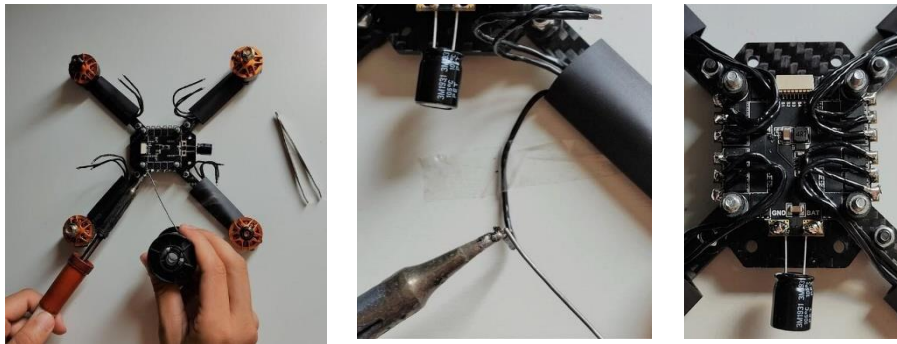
Soldadura del cables dels motors a la placa ESC. Font: Pròpia
